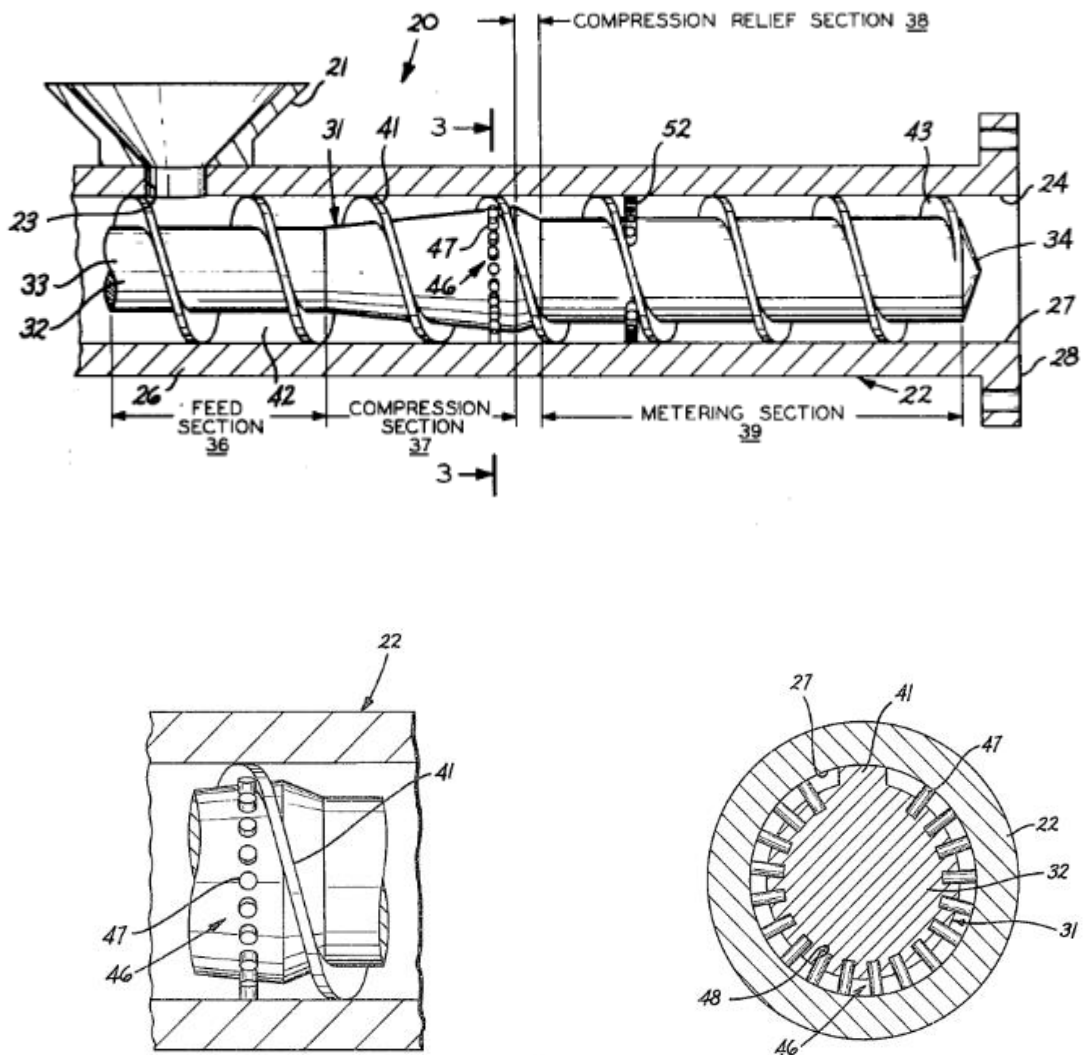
1-вид черв'яка з елевачії в розрізі; 2-детальний вигляд гвинта екструдера; 3-поперечний розріз гвинта
